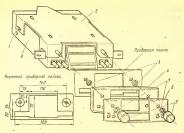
Установка и крепление магнитолы АМ-301 в автомобиле
